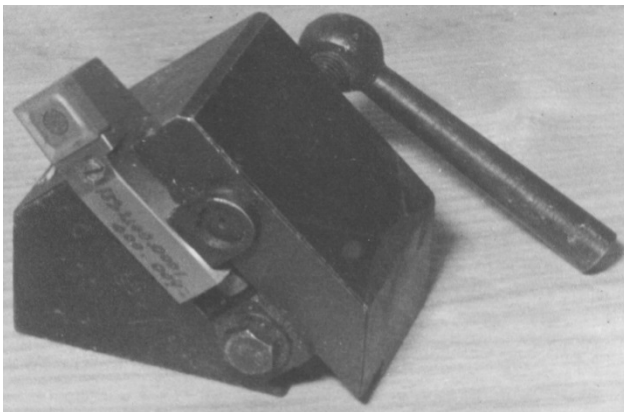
Державка для налагодження прохідного різця на розмір поза верстатом
